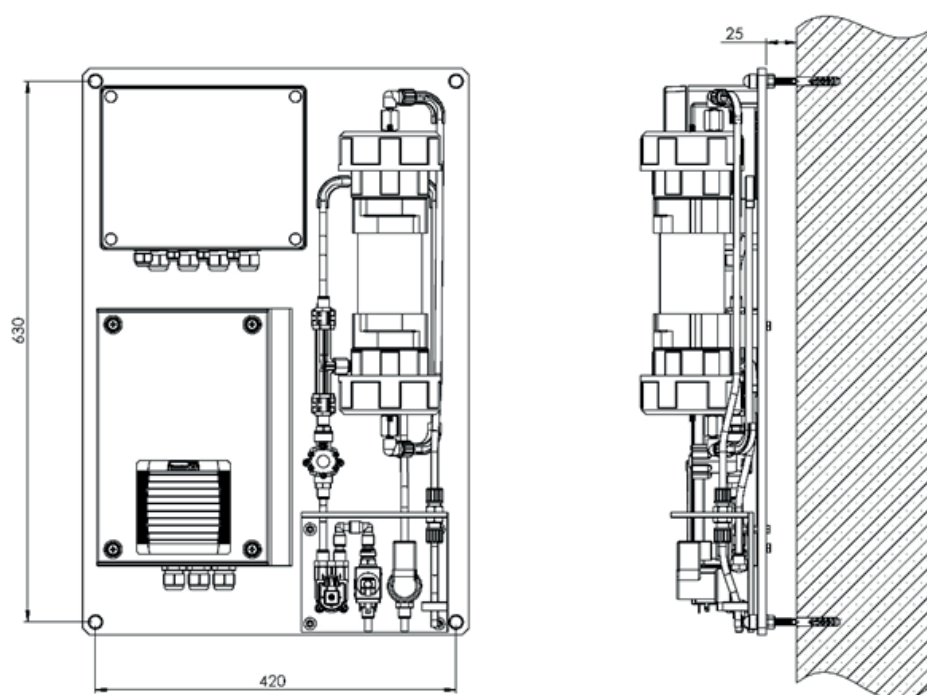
Dimensions de MINICHLORGEN sans couvercle
